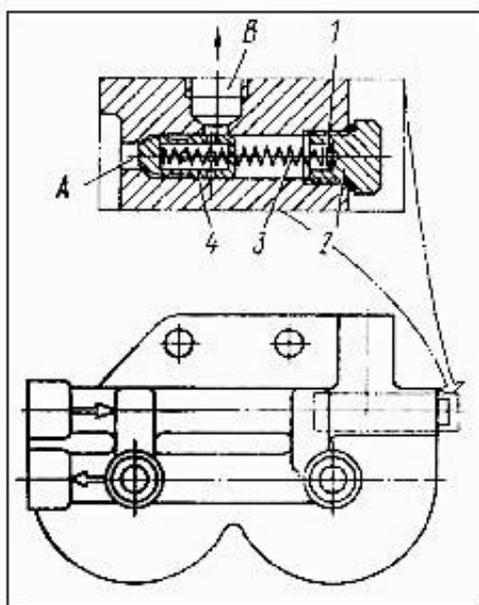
Клапан-жиклер фильтра тонкой очистки топлива Камаз-740:
